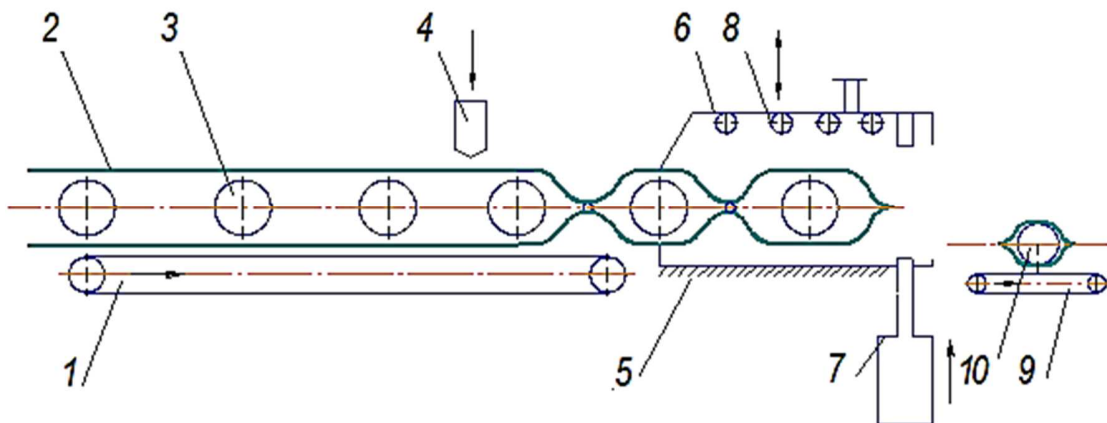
Схема вакуумного пакування: 1 – подавальний конвеєр; 2 – рукавна плівкова заготовка; 3 – упаковувані предмети (порції); 4, 7 – зварювальні ножі; 5 – вакуумний пристрій; 6 – кришка, що герметизується; 8 – нагрівач; 9 – відвідний конвеєр; 10 – упакований предмет
